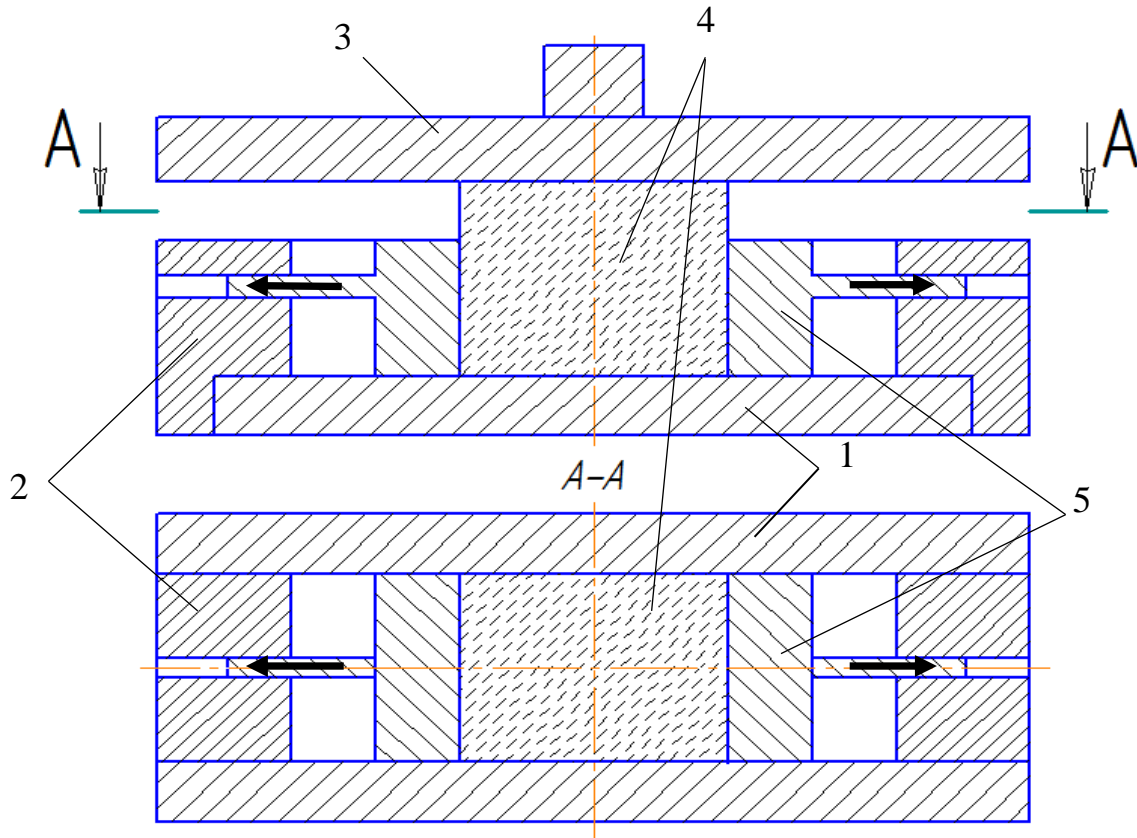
Схема пресс-формы с подвижными боковыми границами
